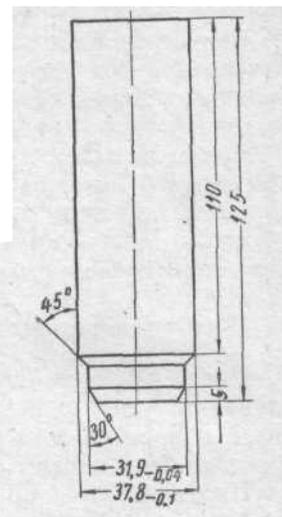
Оправка для развальцовывания трубы рулевой колонки
